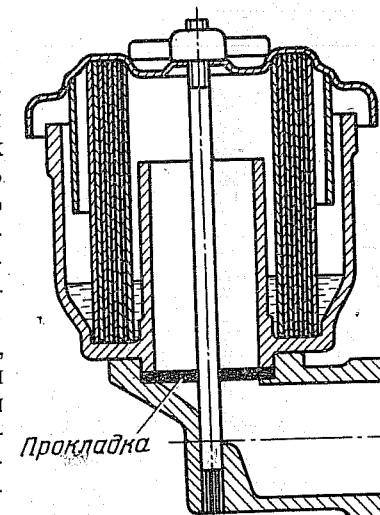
Резиновая прокладка — заглушка под сапун картера двигателя на автомобилях ЗИЛ-164 и ЗИЛ-157К
